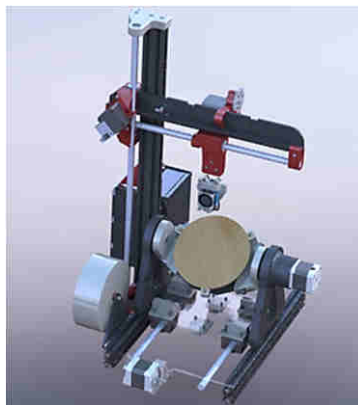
Ensamblaje de diseño CAD mecánico y electrónico del prototipo
